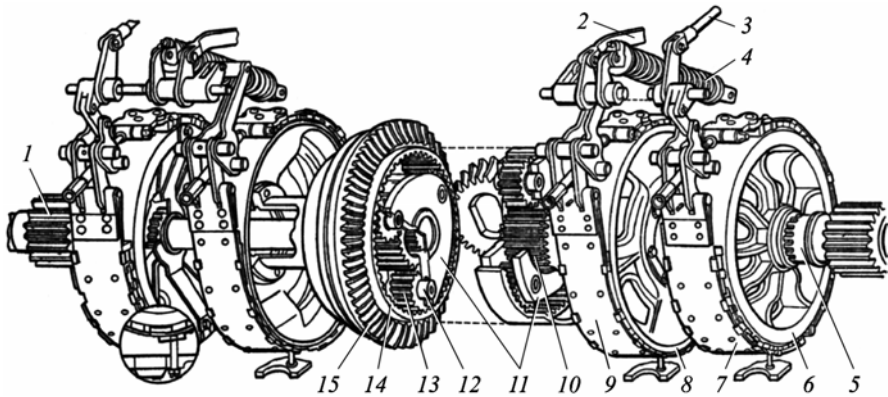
Планетарний механізм повороту ДТ-175С
